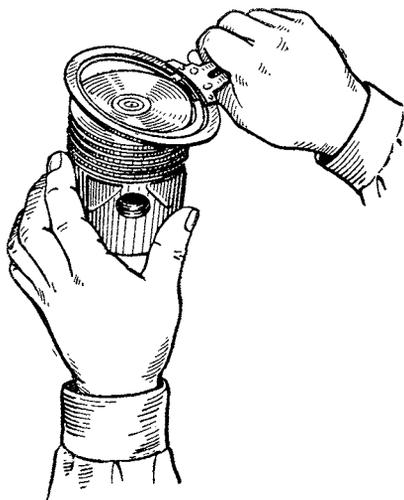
Снятие поршневых колец специальным приспособлением для снятия и установки колец
